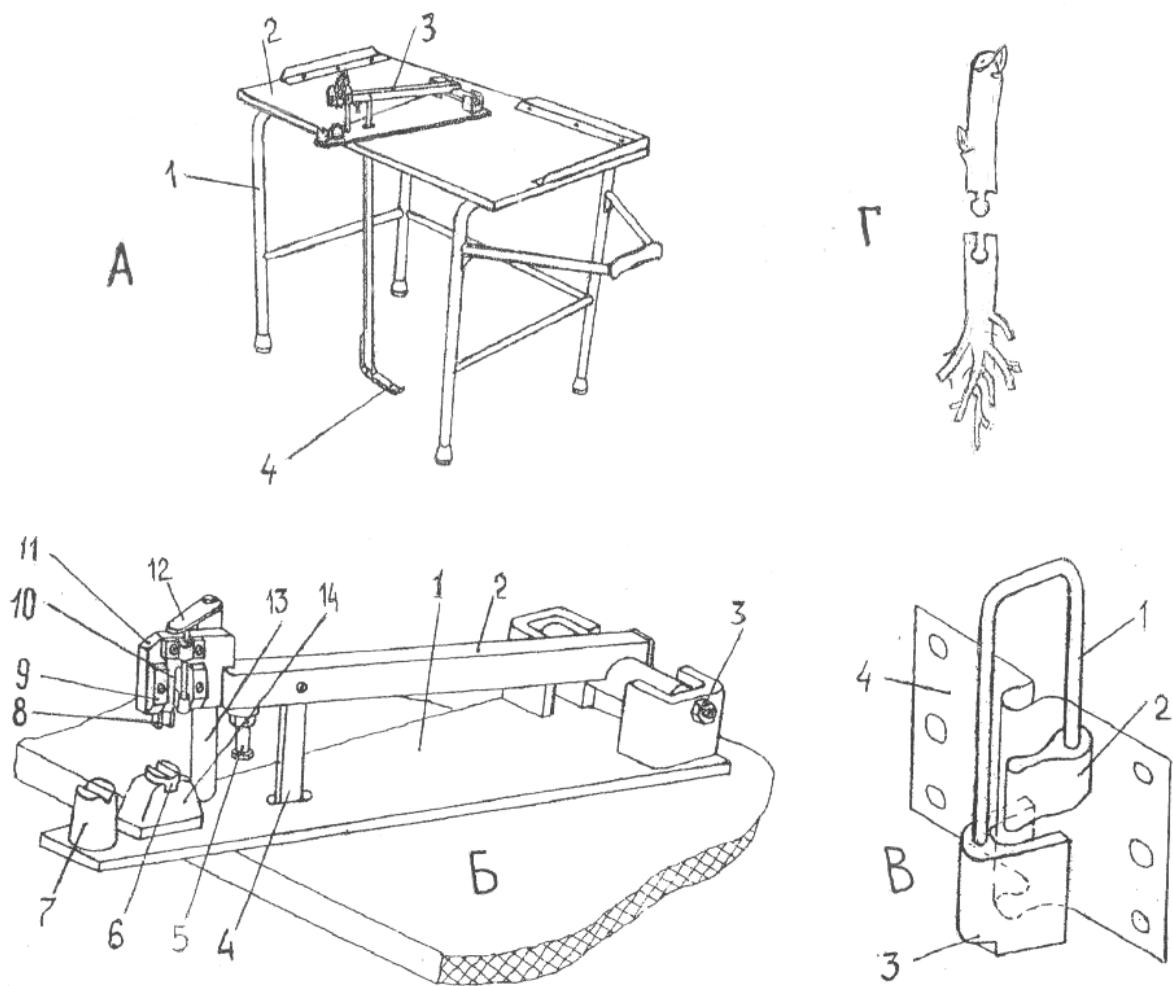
Схема устройства для прививки УПВ. А – внешний вид: 1 – рама; 2 – крышка стола; 3 – режущий механизм с приводом; 4 – привод педальный. Б – режущий механизм: 1 – основание; 2 – рычаг; 3 – центр; 4 – тяга привода; 5 – болт ограничения ходы рычага; 6 – противорез; 7 – подставка для сборки прививок; 8 – выталкиватель; 9 – накладка; 10 – нож фигурный; 11 – суппорт; 12 – упор выталкивателя; 13 – стойка; 14 – стойка противореза. В – омегаобразный нож с выталкивателем: 1 – стержень; 2 – флажок; 3 – скоба; 4 – нож фигурный. Г - вид выполненного омегаобразного среза
